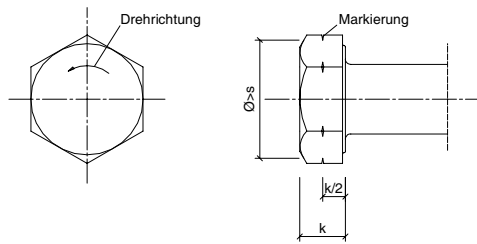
Beispiel zur Kennzeichnung von Linksgewinden
